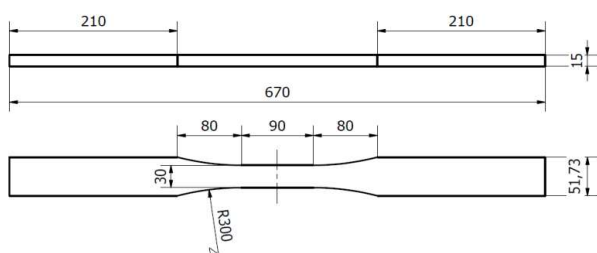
Esquema de la geometría de las probetas con borde recto (cotas en mm).
